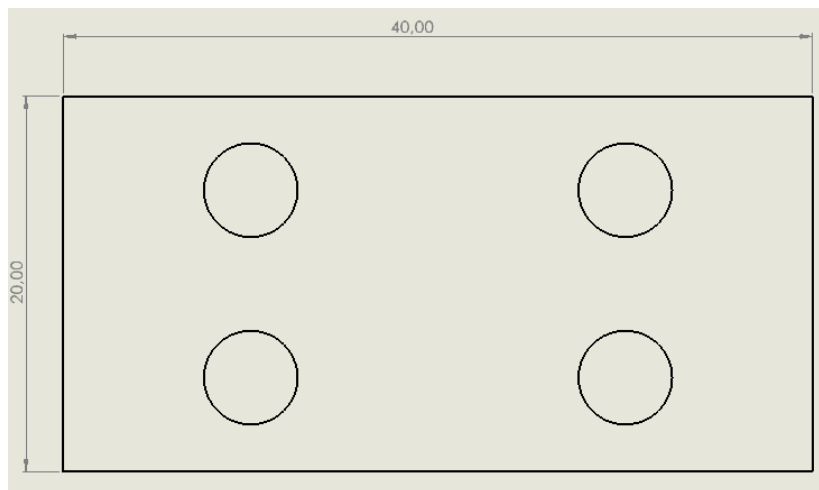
Vista frontal: Cotas das chapas do ângulo reto em milímetros. (Autor, 2021)
